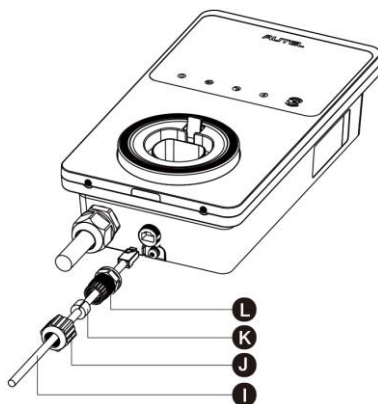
Collegamento del pressacavo Ethernet waterproof
